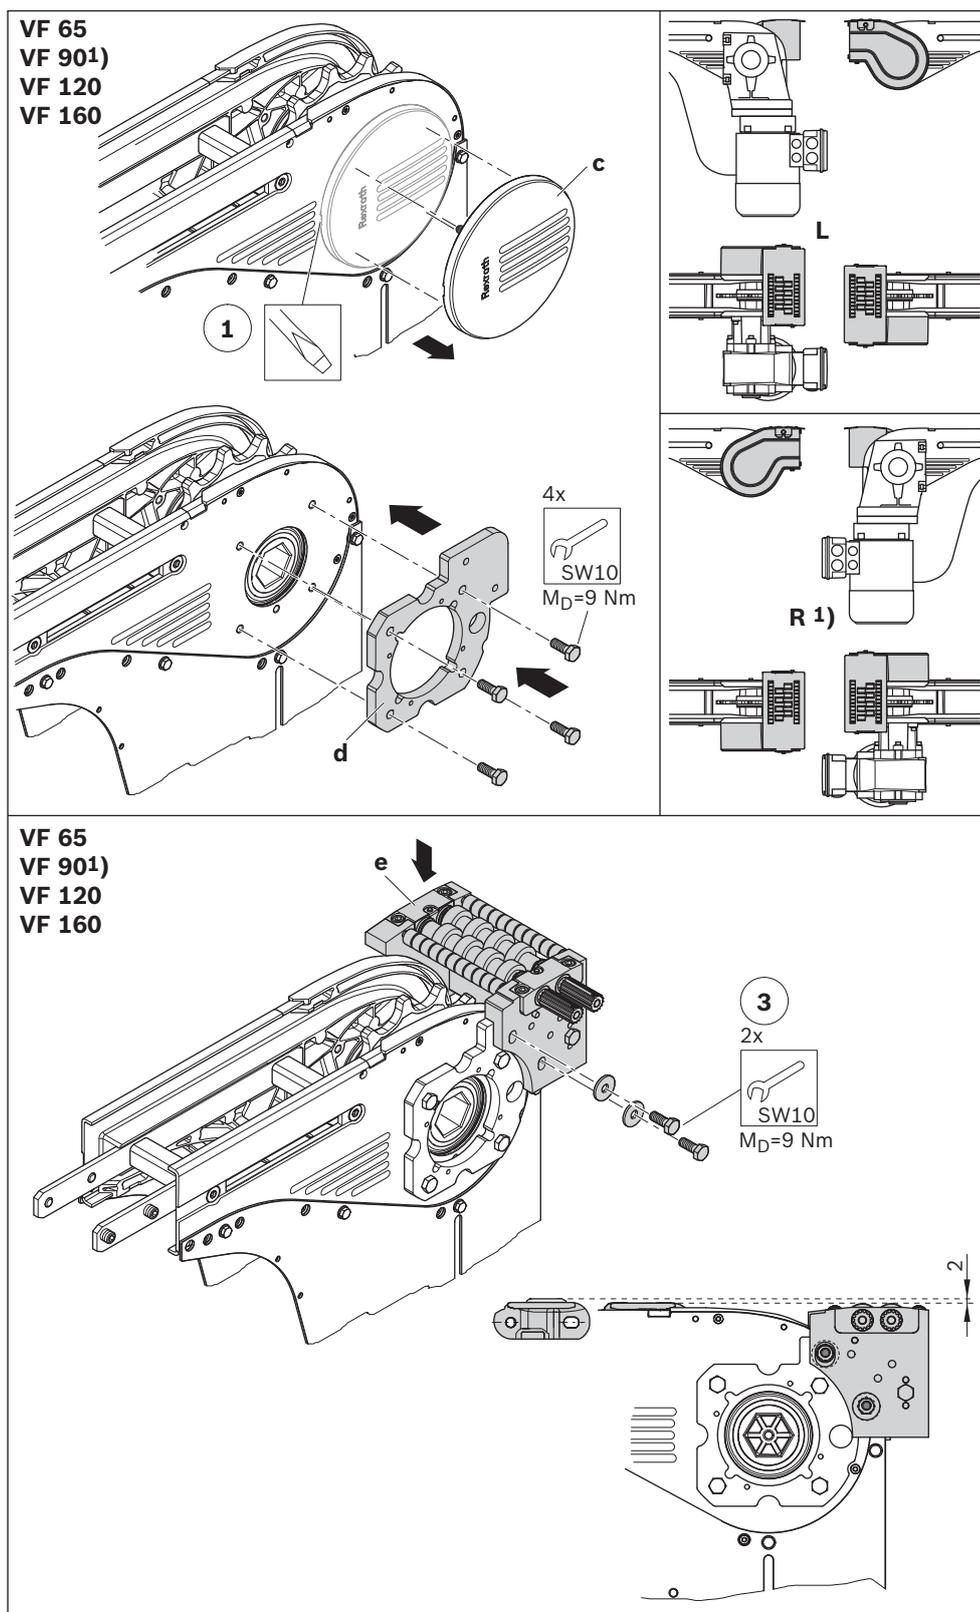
Montaggio del set di collegamento attivo, collegamento alla macchina (1/3)
